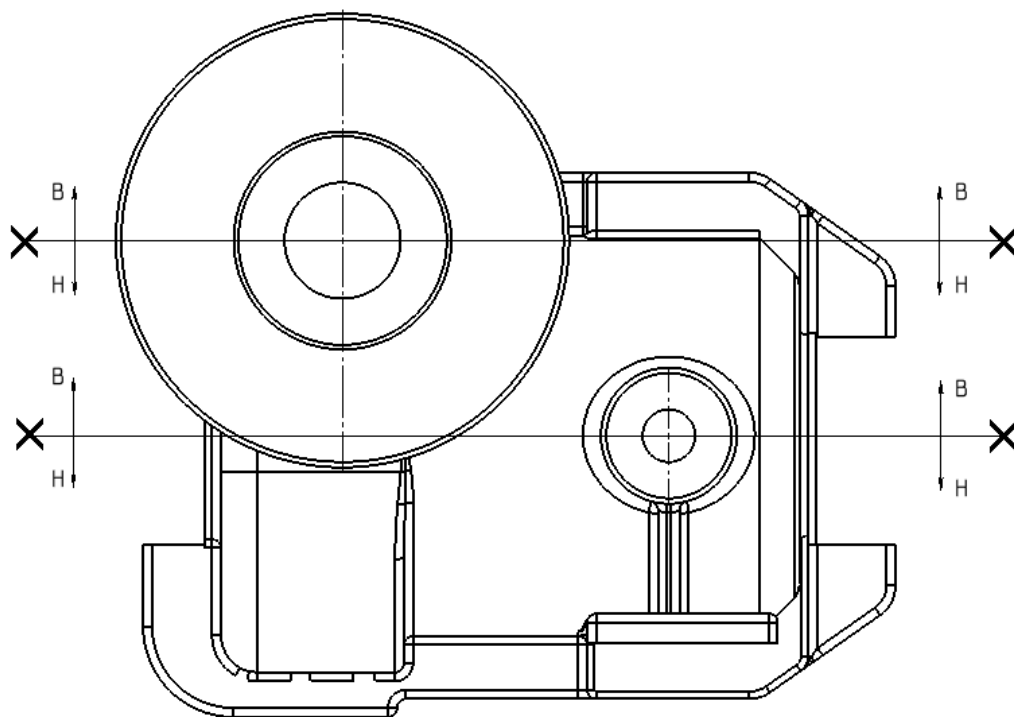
Ескіз заготовки з двома опоками рознімання
